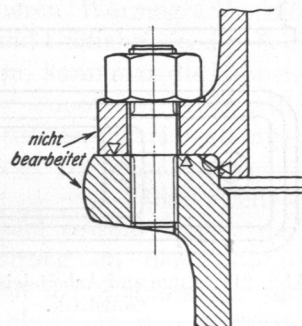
Einschränkung der Bearbeitung durch geeignete Formgebung.
